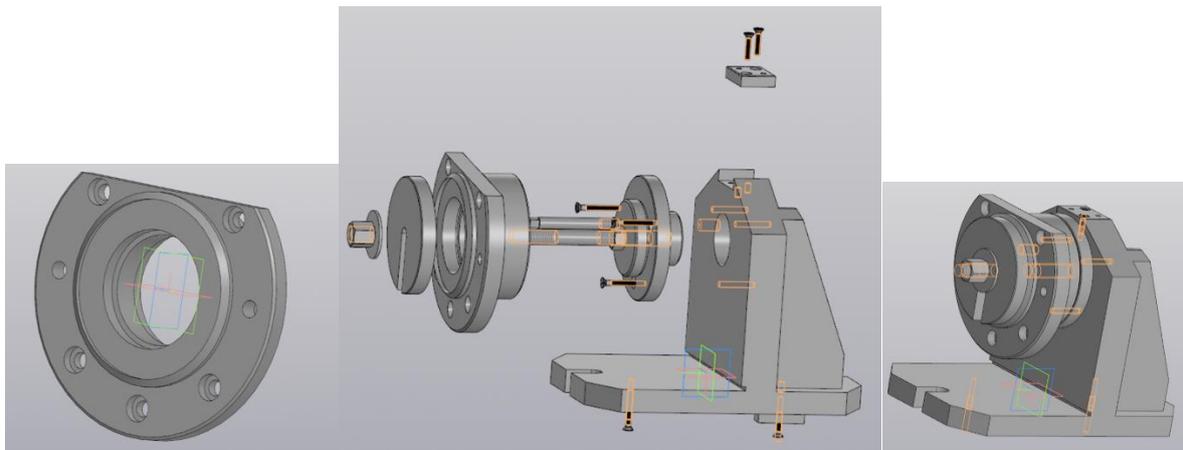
3D-модели детали “Втулка” (слева) и фрезерного приспособления (справа)
